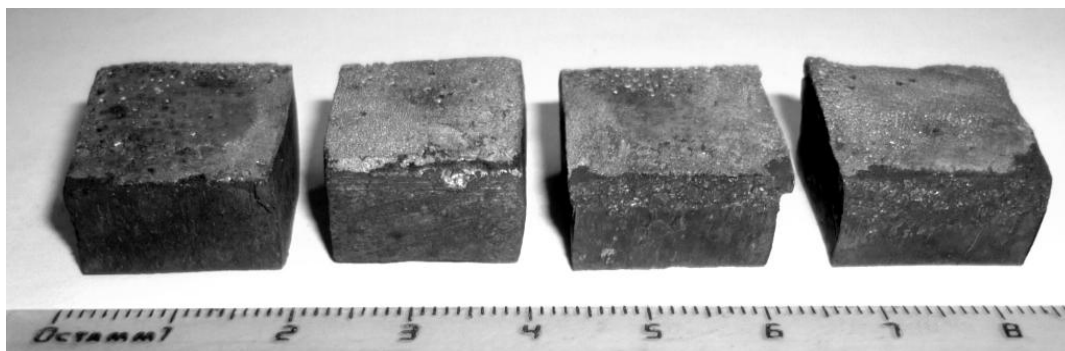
Внешний вид образцов, наплавленных самофлюсующимися твердыми сплавами
